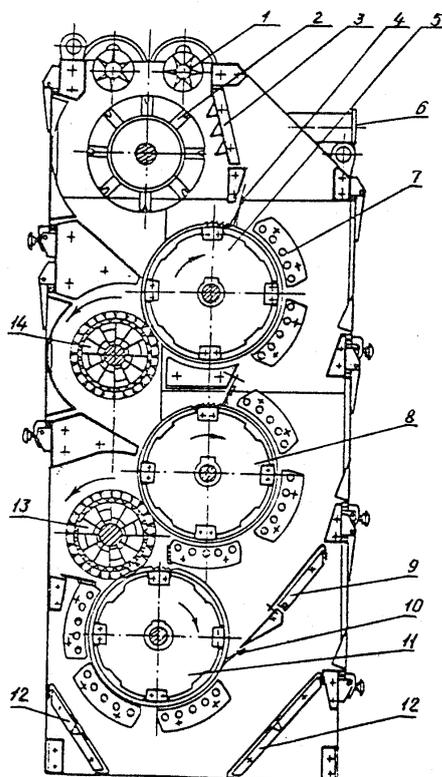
Схема очистителя крупного сора марки ЧХ-5
